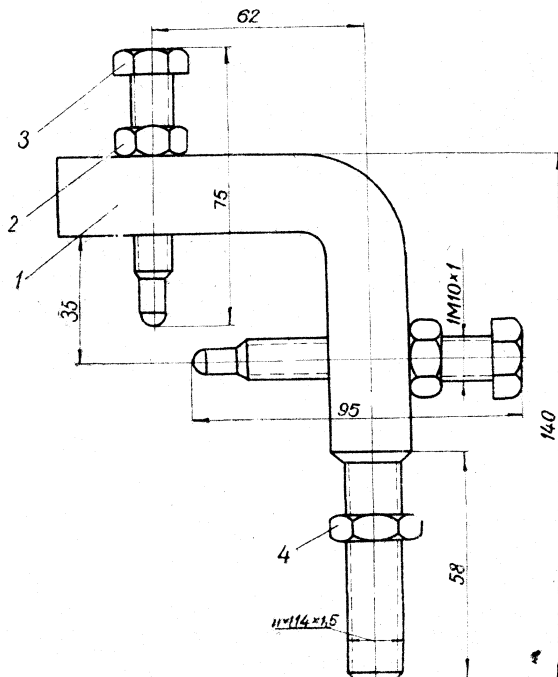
Эскиз приспособления для центрирования дизеля 1Д6-150.
